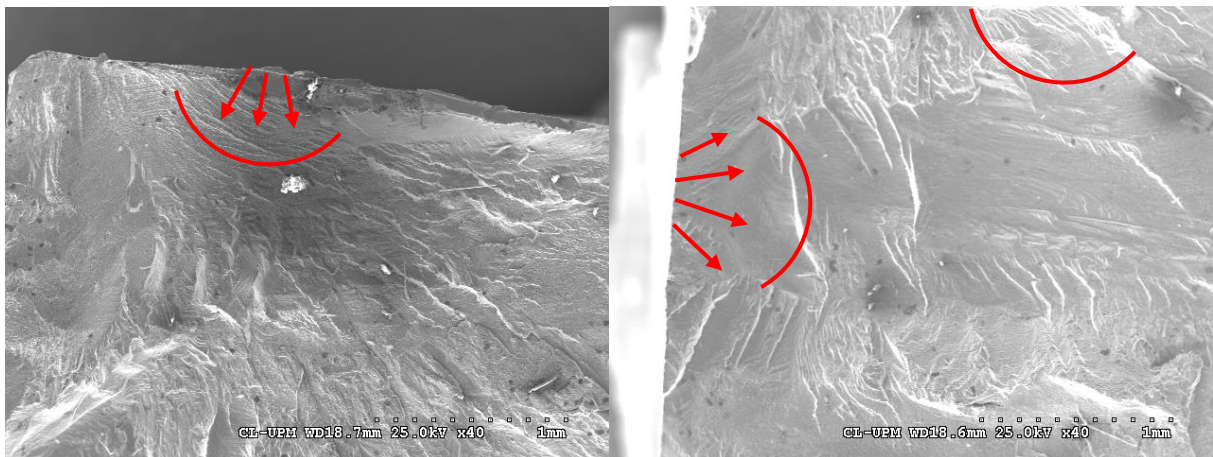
Inicio de grieta de fatiga en la zona superior (izquierda) y lateral (derecha) de la probeta 7
